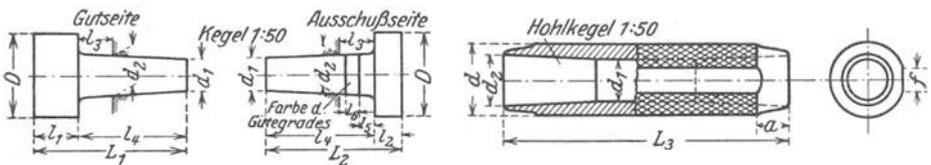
44. Toleranzlehndorn mit Einsteckgriff nach DIN.
